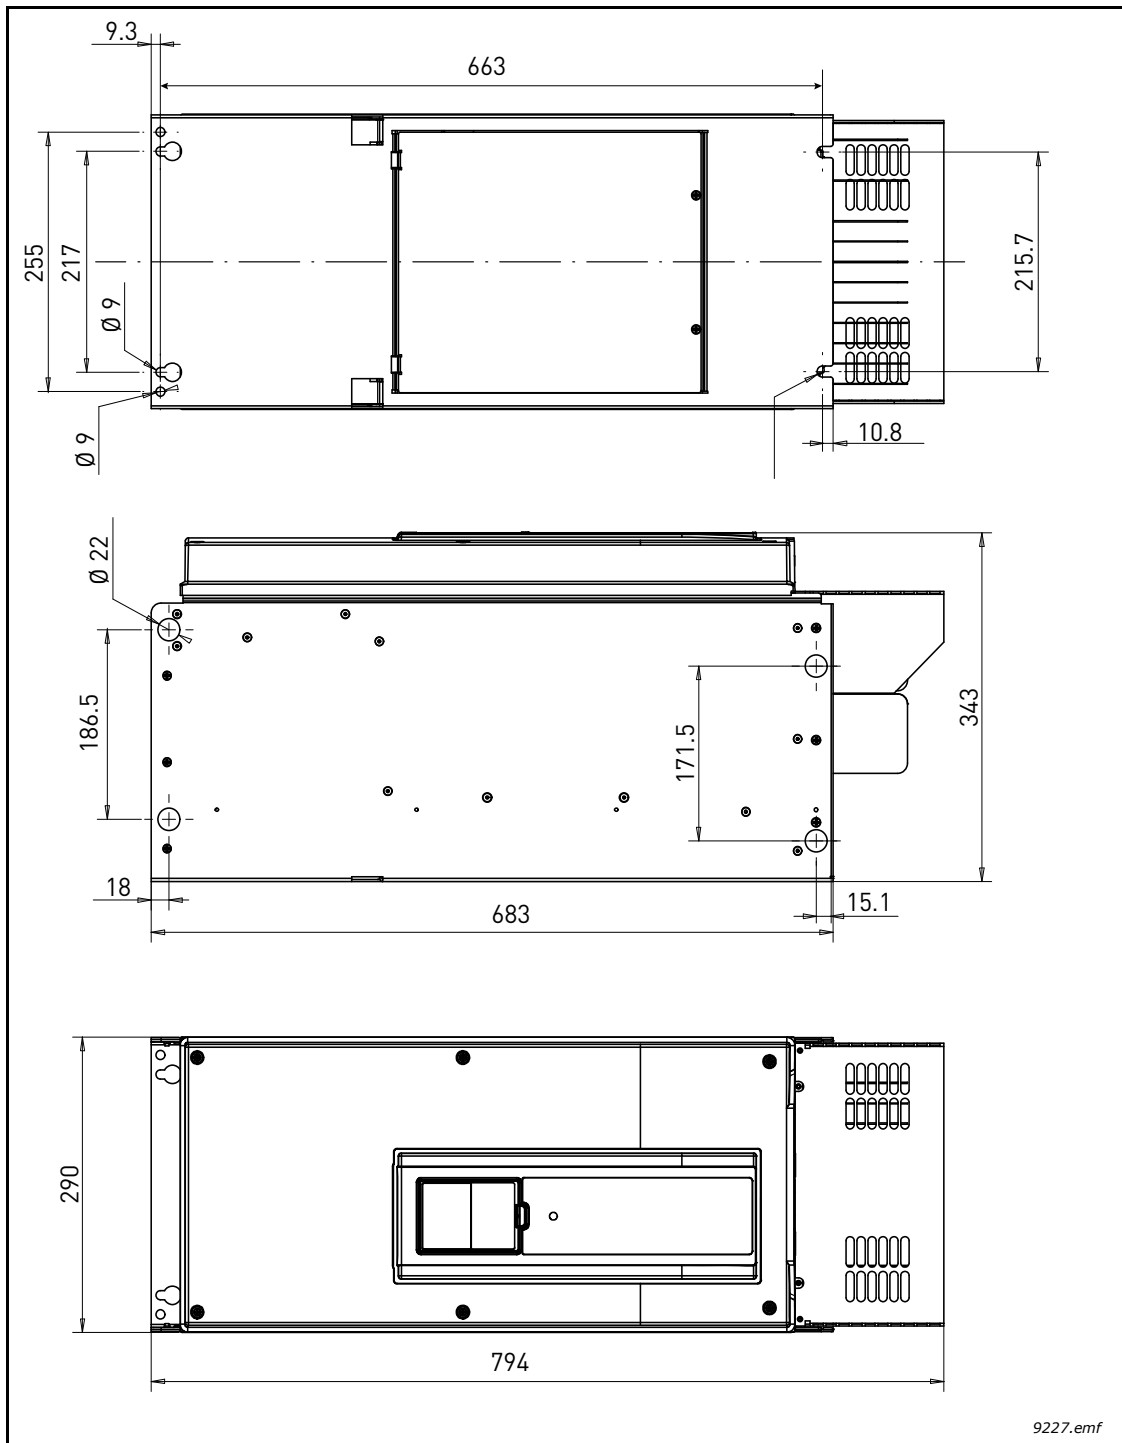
Dimensões do inversor de CA Vacon, MR8 IP00
